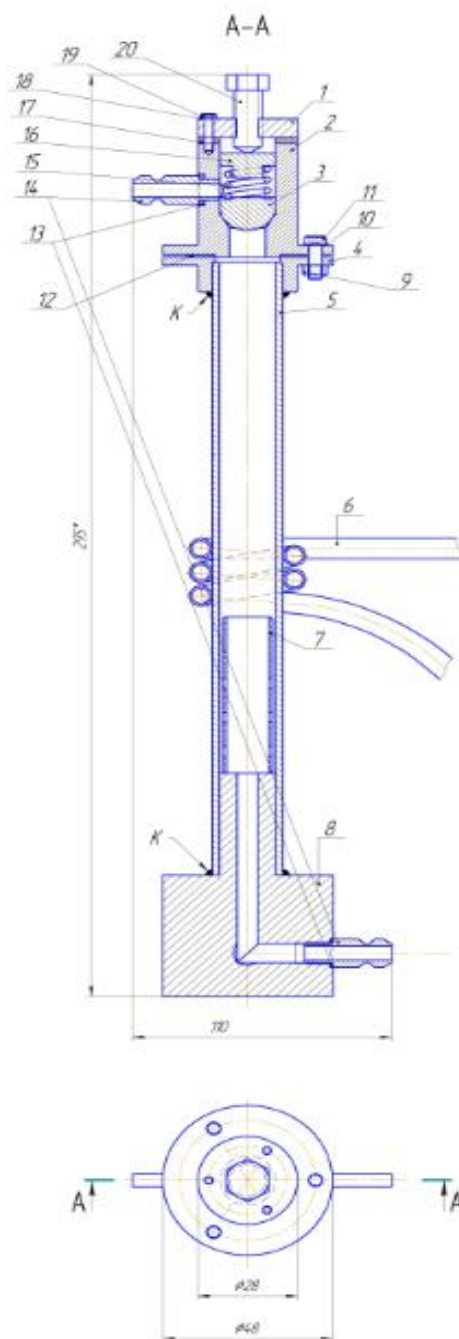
Камера для химико-термической обработки образца из быстрорежущей стали
